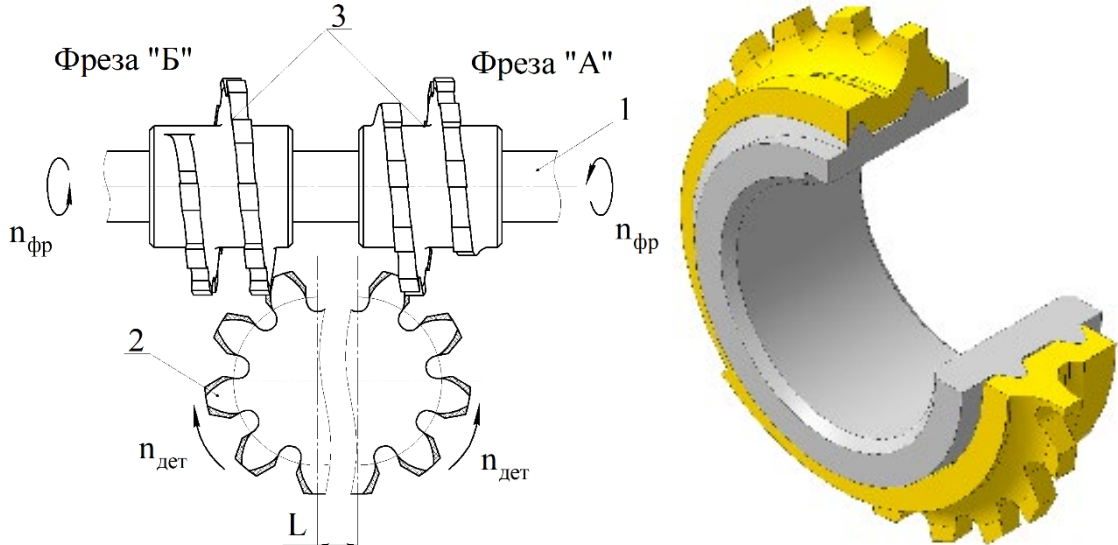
Робочі рухи та переміщення при черв'ячно-контурному зубофрезеруванні
